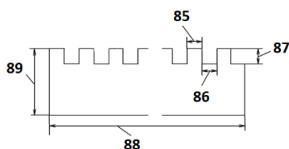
Развертка бортика датчика с геометрическими размерами выступов и углублений на гребне (и на кромке) бортика.
